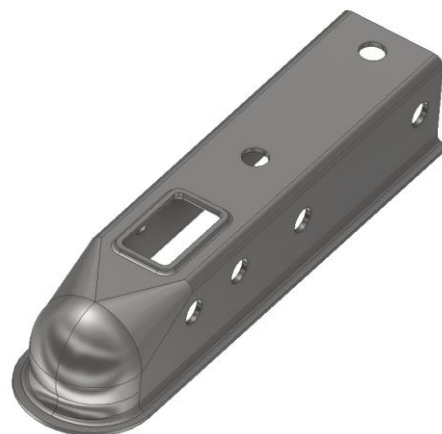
Příklady součástí vyrobených tažením [4], [5], [6]
